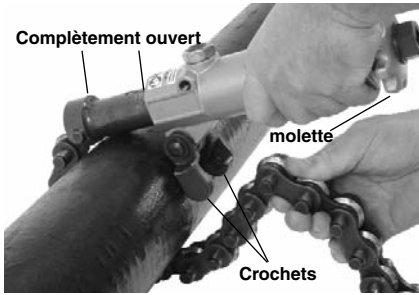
Coupe-tubes complètement ouvert pour l'engagement de la chaîne
